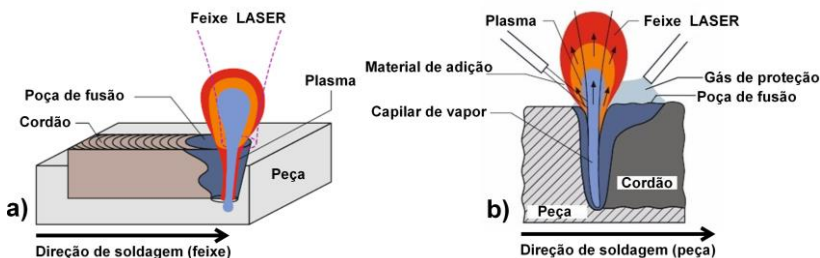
Ilustração do processo de soldagem LASER no modo *keyhole* (Adaptado de [1])
